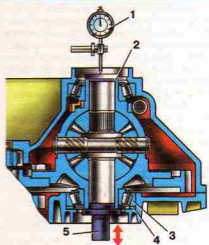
Схема подбора толщины регулировочного кольца подшипников дифференциала: 1 - индикатор; 2 - опорная оправка; 3 - подшипник дифференциала; 4 - установочное кольцо; 5 - оправка
